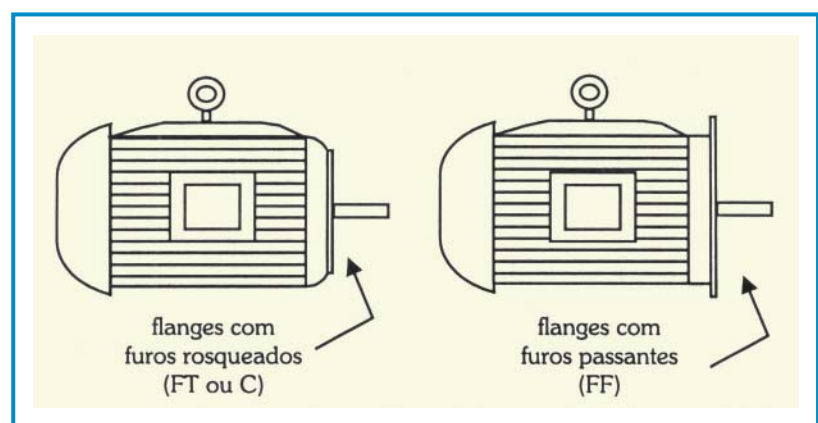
Flanges com Furos Rosqueados, fFlanges com Furos Passantes
